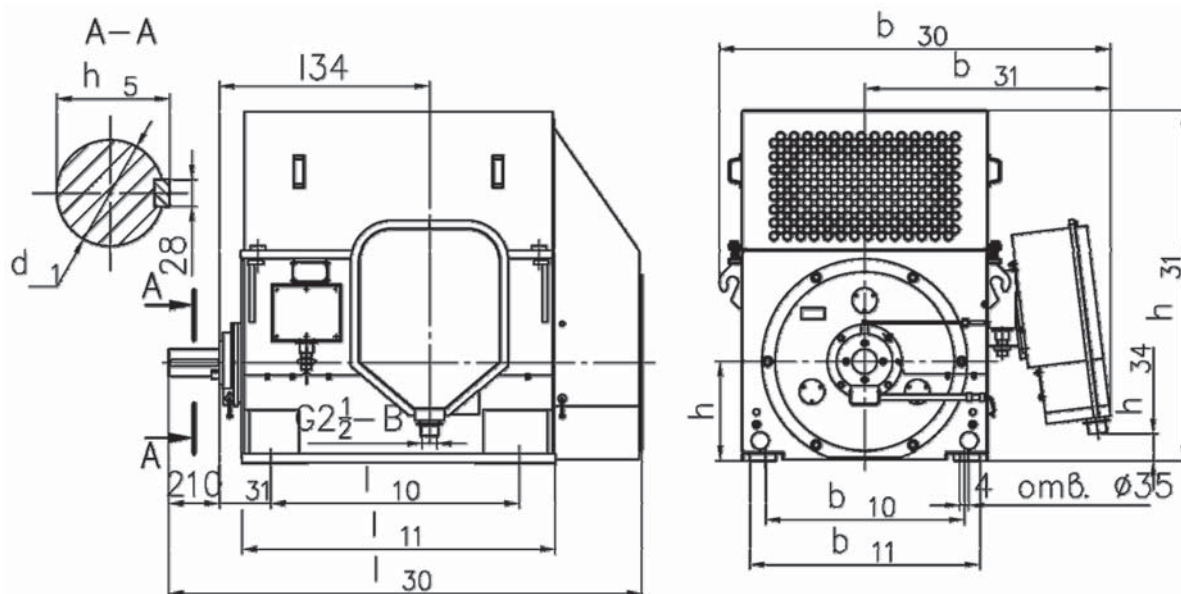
Электродвигатели серии ДАЗО со сварной коробкой
